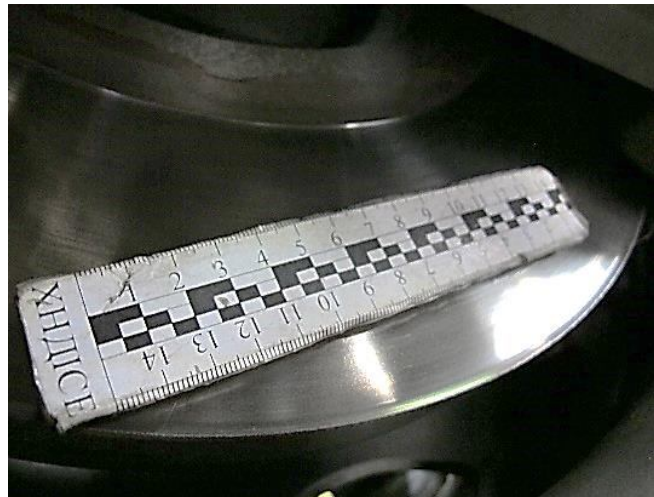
Детальний вигляд поверхні гальмівного диска правого заднього колеса автомобіля MAN TGM
